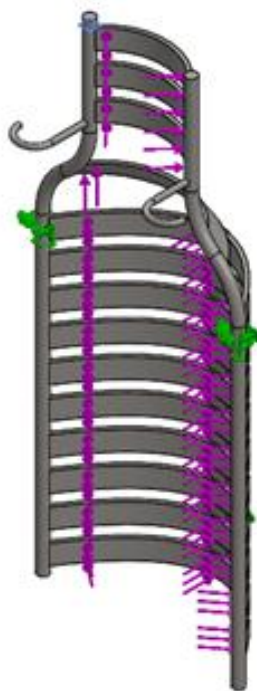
Fuerzas y sujeción de la parte superior de la camilla.
